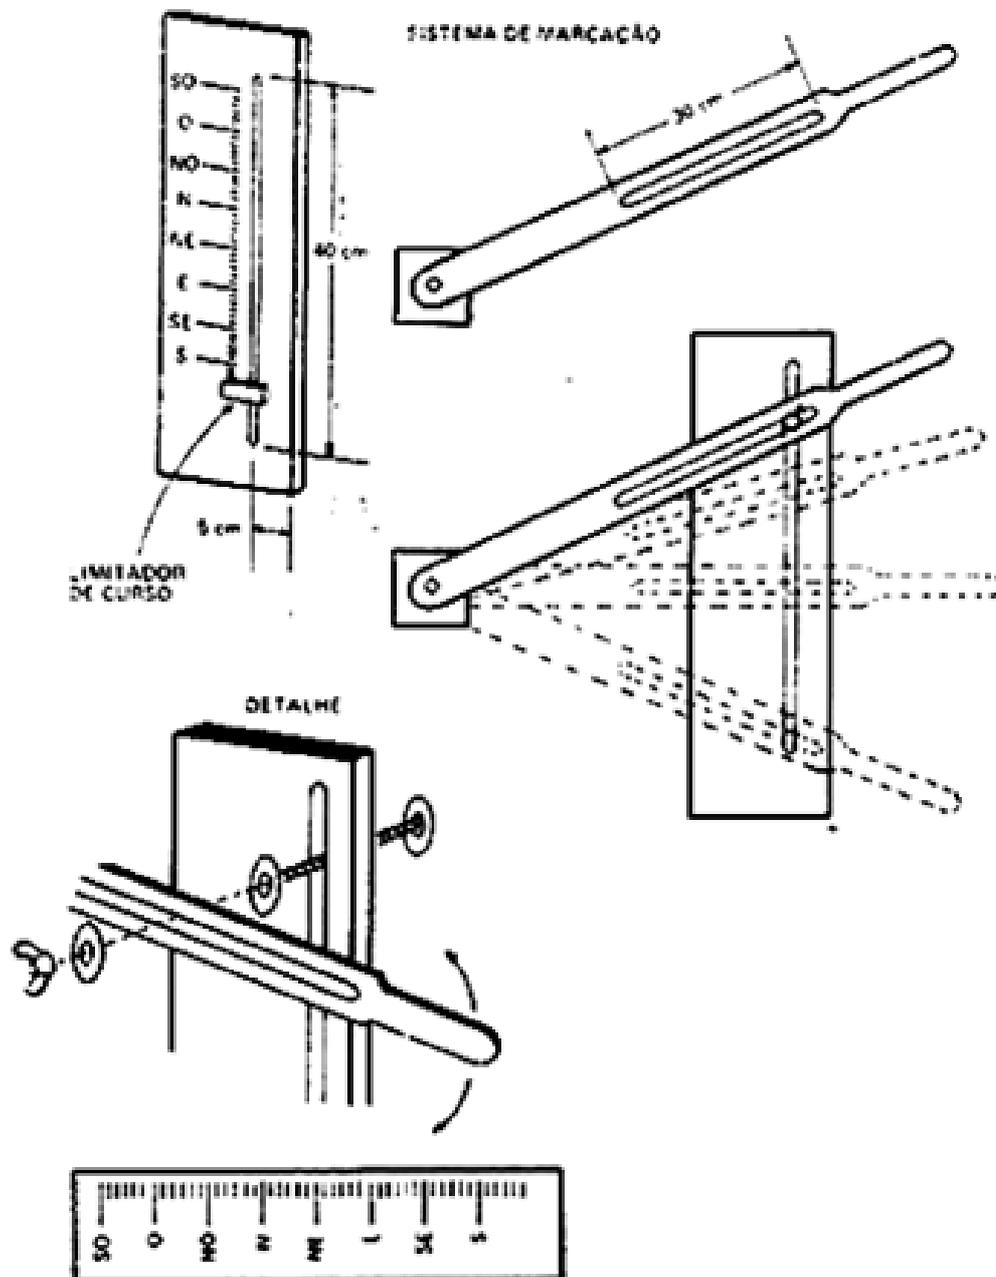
Detalhes da alavanca de posicionamento, sistema de fixação e marcador de posição do rotor manual de antenas.
